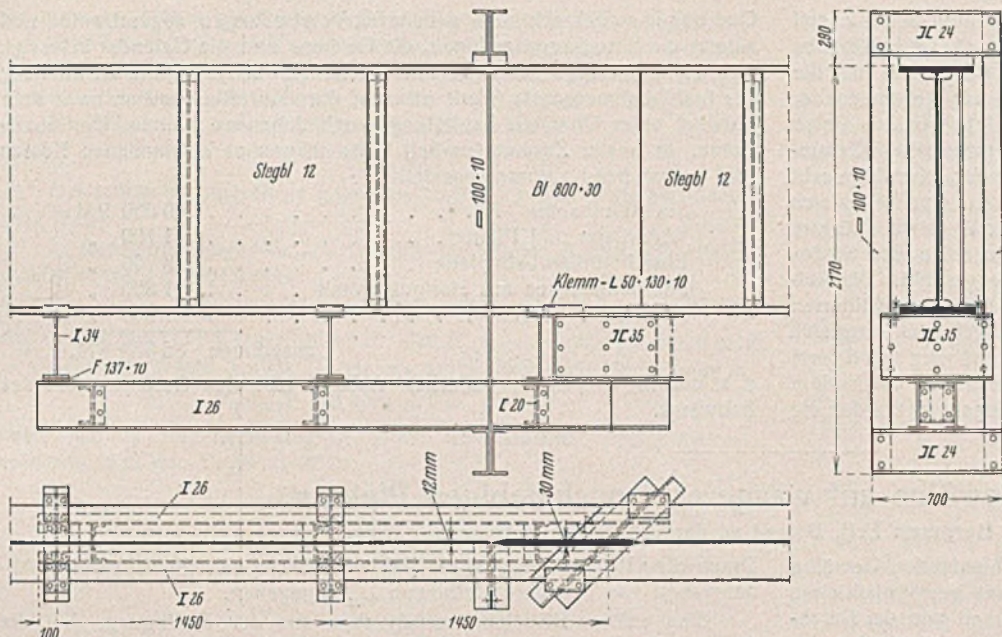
Klemmvorrichtung zum Schweißen.
